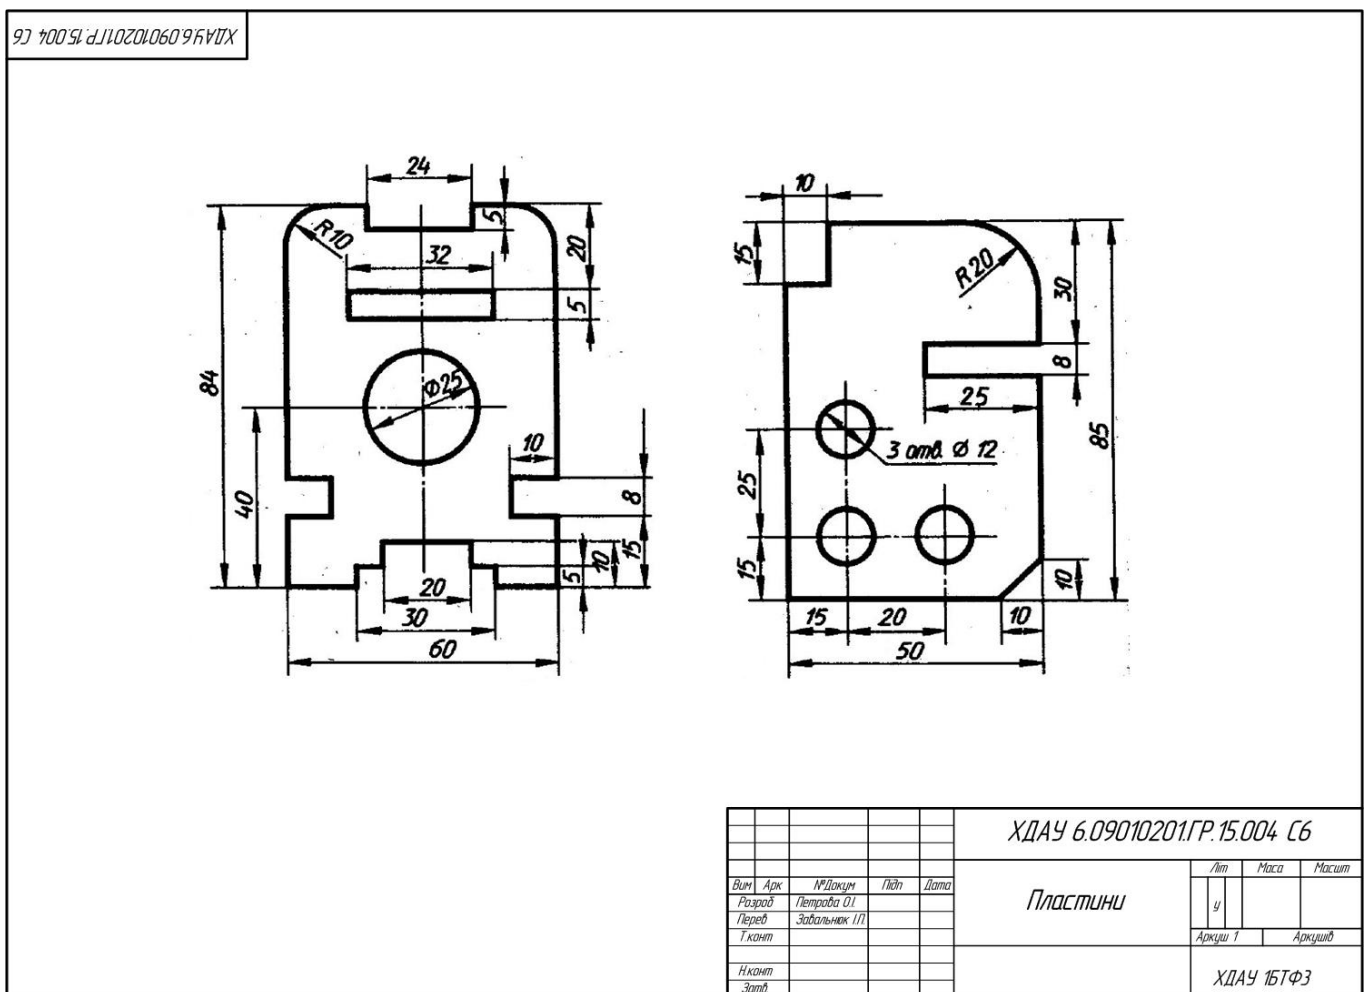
Приклад виконання креслення пластин з розмірами
